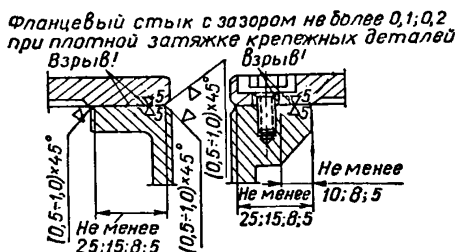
Допуски прилегающих поверхностей при затянутых болтах или клиновом креплении
